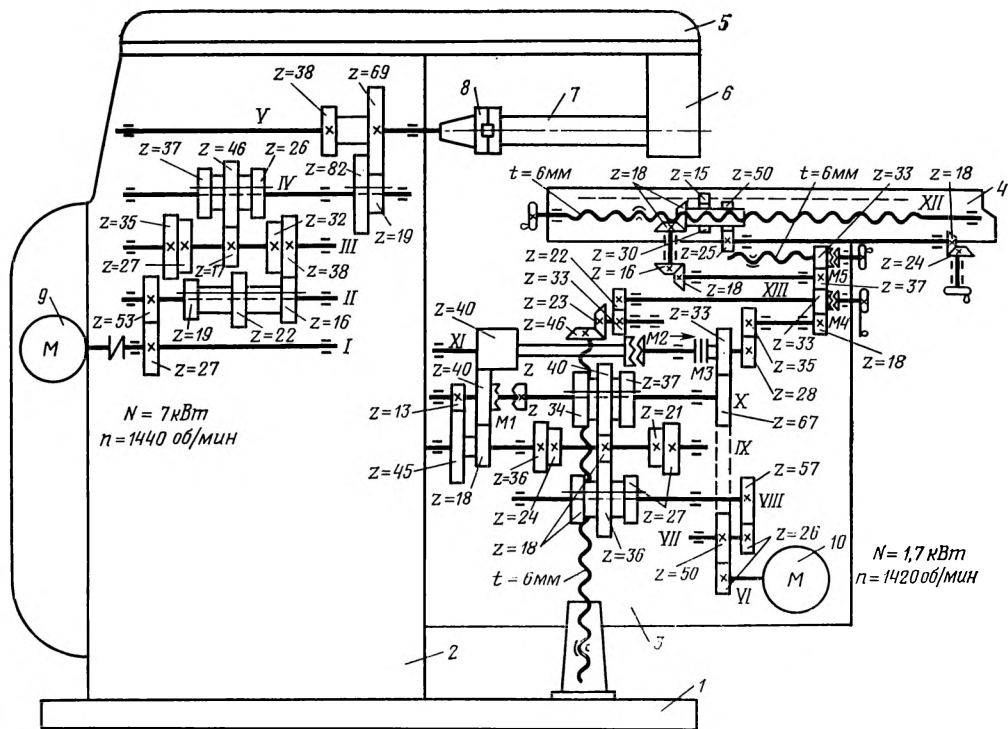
Кинематическая схема универсального горизонтально-фрезерного станка модели 6М82
